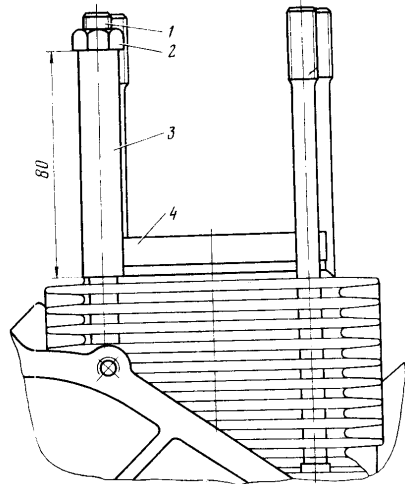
Крепление цилиндров на картере коленчатого вала: 1 — шпилька крепления головки цилиндров; 2 — гайка; 3 — трубка; 4 — цилиндр
